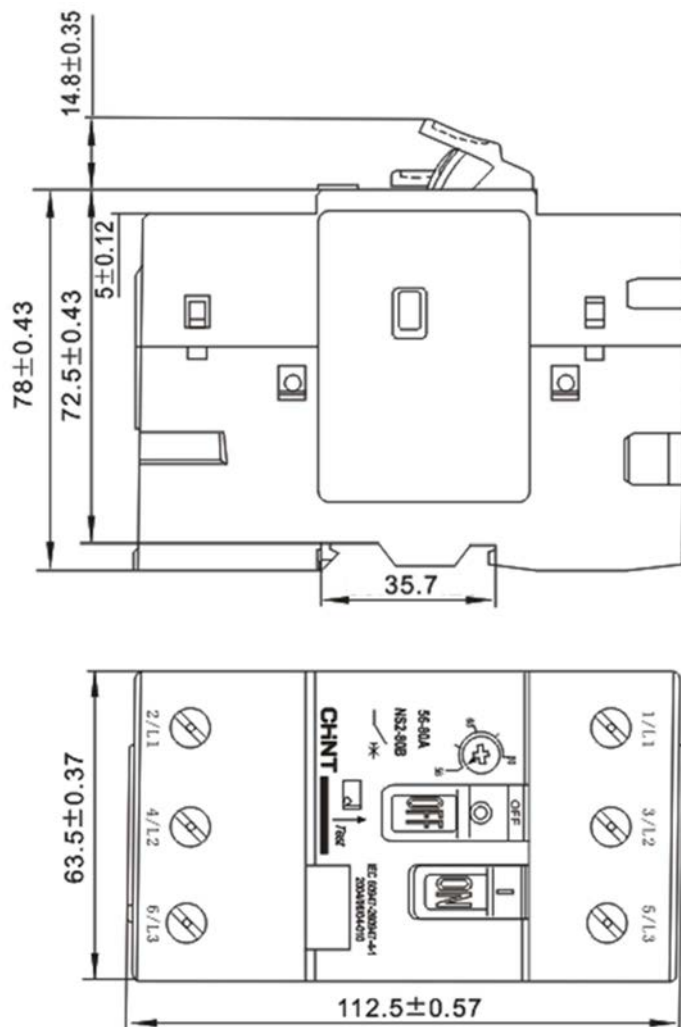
Габаритные и присоединительные размеры NS2-80B
